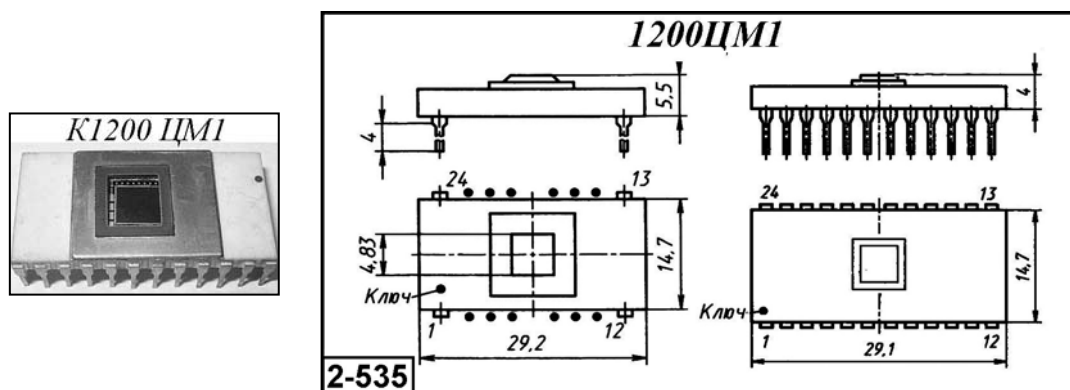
Внешний вид и габаритные размеры 1200ЦМ1
